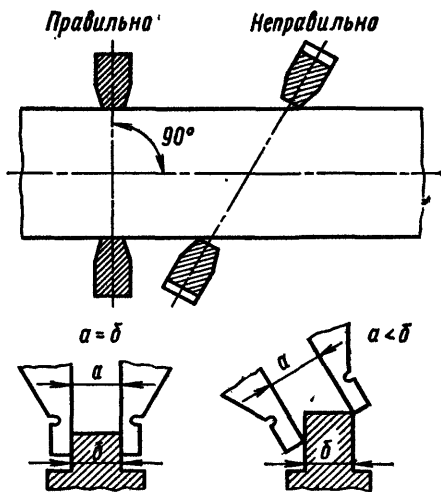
Установка штангенциркуля при измерении наружных поверхностей
